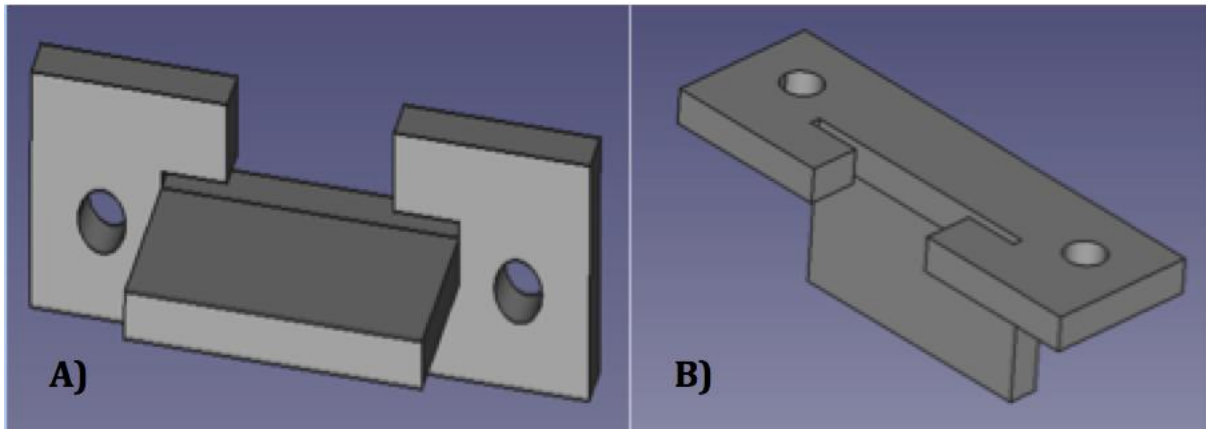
Modelo 3D de la tapa de la bomba de inyección que ancla la émbolo a la pieza móvil de la bomba de inyección. Se muestra la vista plantar (A) y frontal (B) de la.tapa.
